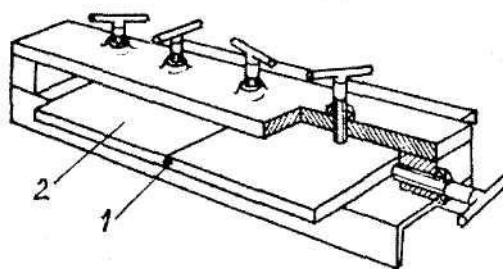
Приспособление для сборки пластин: 1 — прихватка; 2—пластина.
